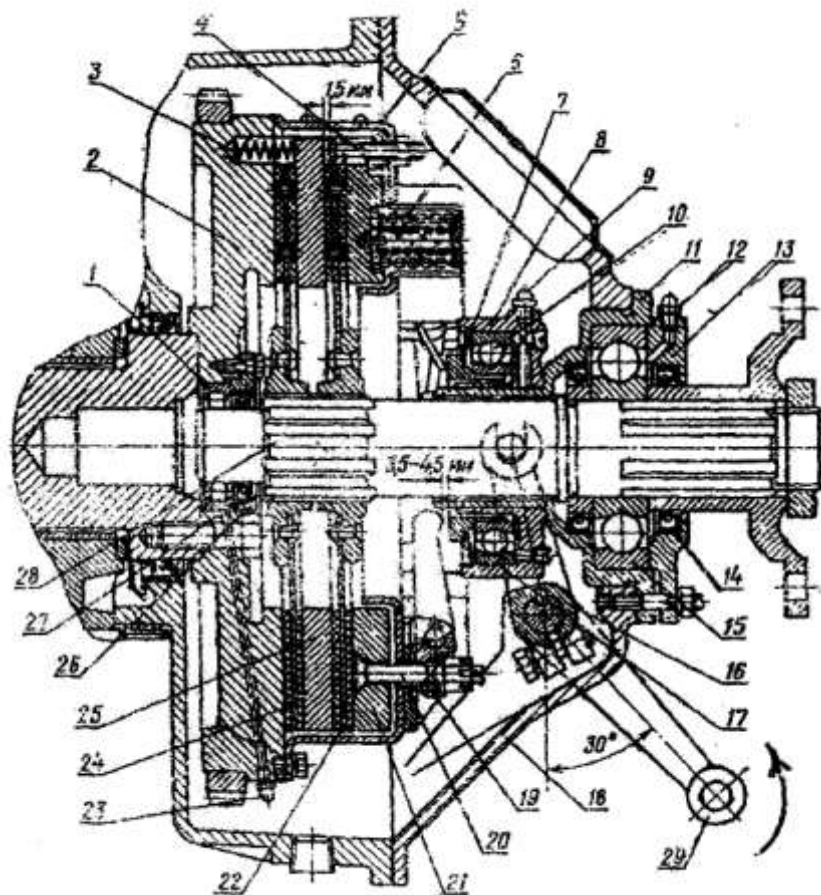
Двухдисковая муфта сцепления трактора:
